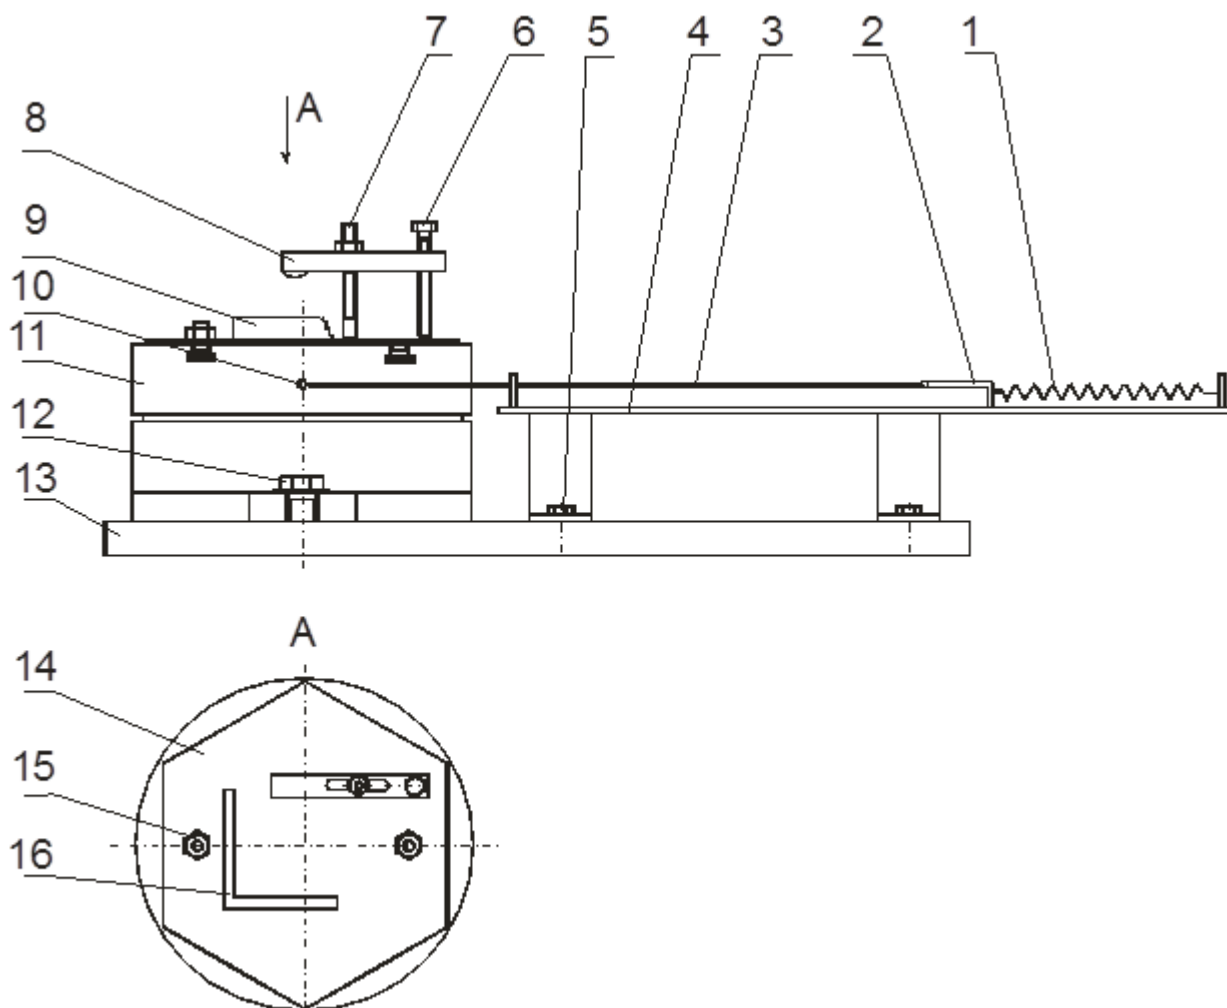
Экспериментальная установка: 1 — пружина; 2 — ползун; 3 — трос; 4 — планка; 5 — основание; 6 — болт; 7 — гайка; 8 — консоль; 9 — угол; 10 — болт; 11 — поворотный стол; 12 — болт; 13 — основание; 14 — пластина; 15 — болт
